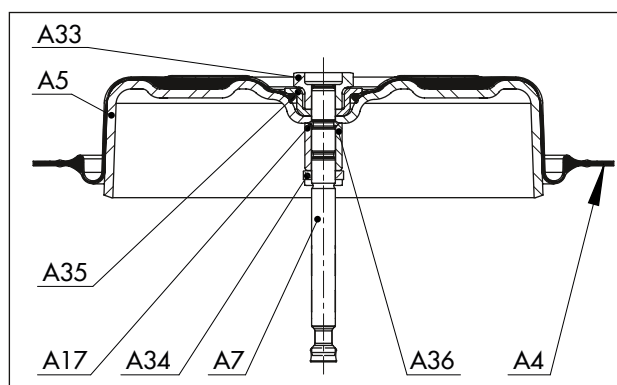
Disposición de las piezas, sentido de actuación FE (750v2 cm²)
